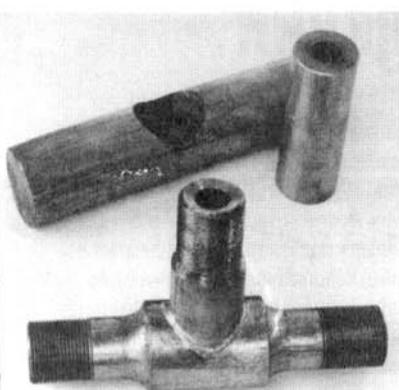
Заготовка и паяный тройник трубопровода высокого давления
